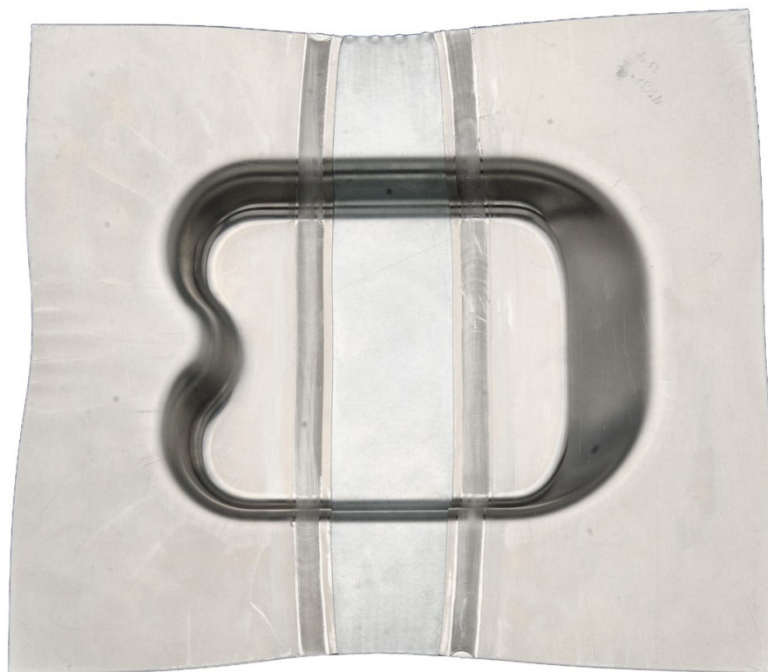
Tailor Welded Blank in Aluminium-Stahl-Mischbauweise – im Rahmen des Projektes gefertigter Demonstrator
